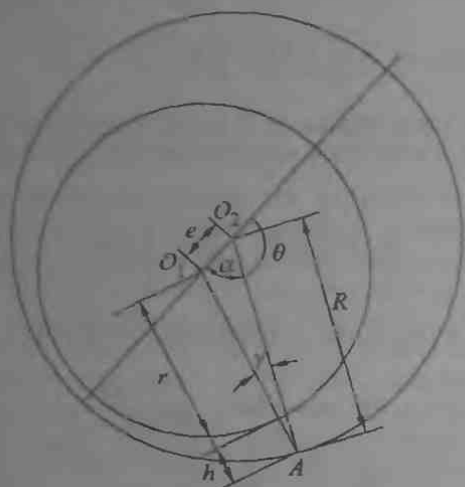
Геометрия смазочной пленки вала и вкладыша
